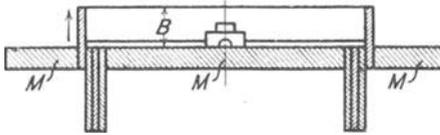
Abformen einer Riemenscheibe auf einer Teleskop-Formmaschine.
